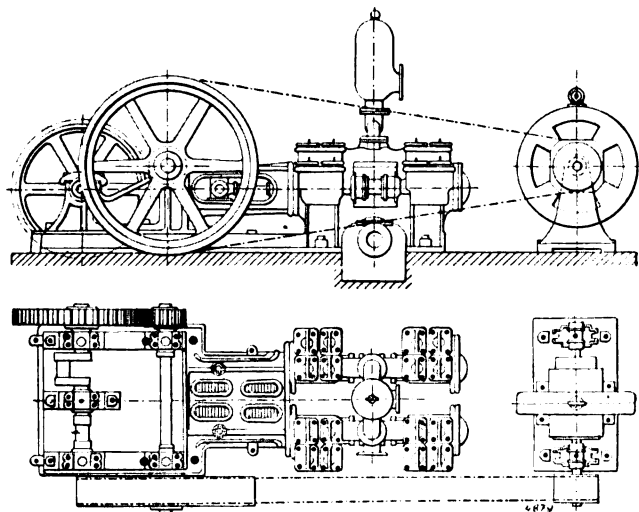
Pompe double actionnée par courroie et engrenages.
